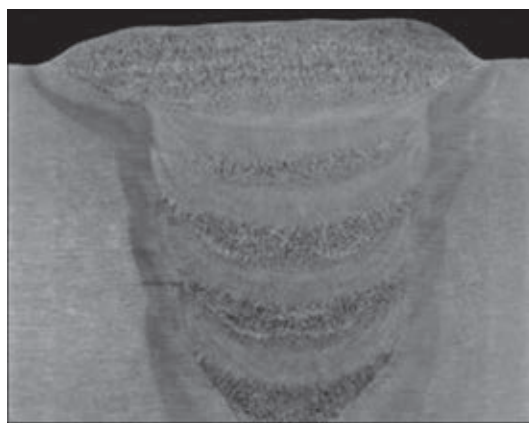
Макрошлиф (увелич. 3,5) сварного соединения, выполненного рутиловой порошковой проволокой
